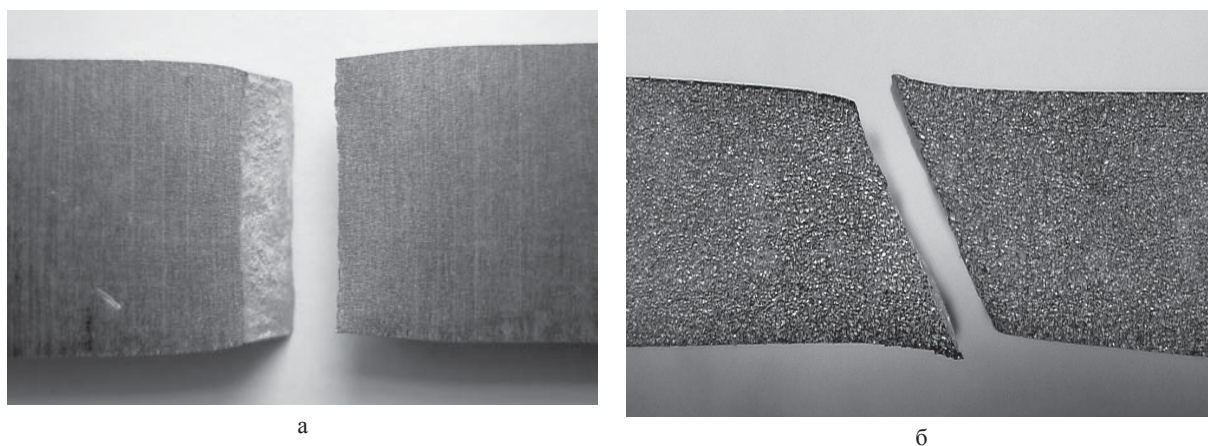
Разрушенный образец без сварного соединения: а — вид сверху; б — вид сбоку
